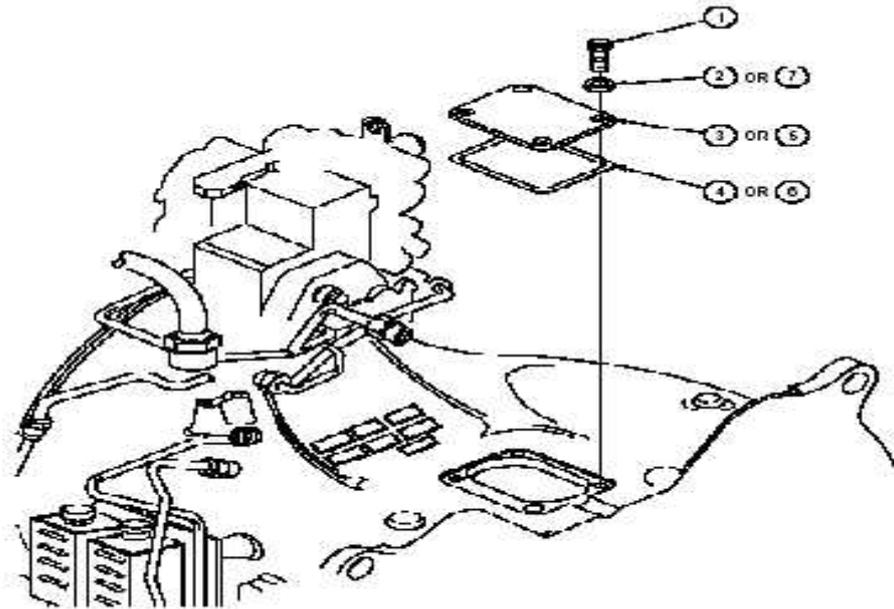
inspection boroscopique des ailettes du 2eme étage de la turbine libre.
